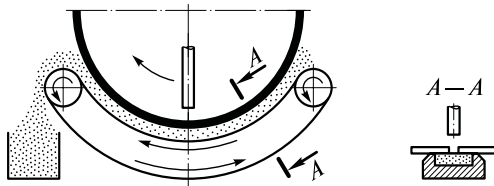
Флюсоремная подушка для сварки кольцевых швов
